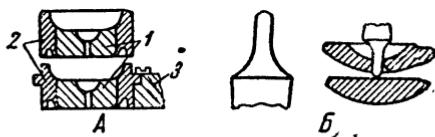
А—способы крепления шатонов: 1—камень; 2—бушон; 3—платина; Б—схема расположения конца оси баланса, сквозного и накладного камней
